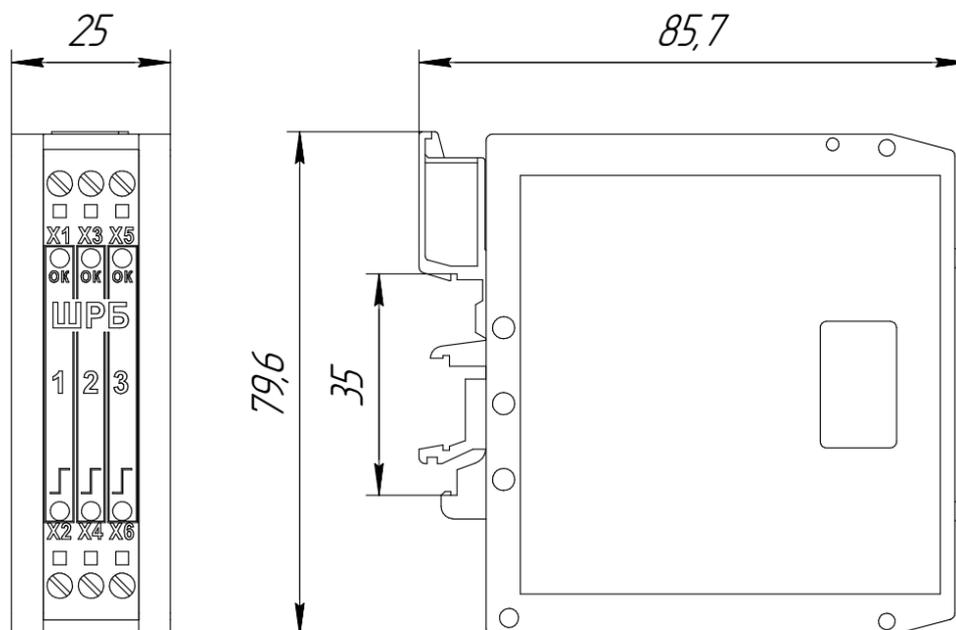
Габаритный чертеж ШРБ-17
